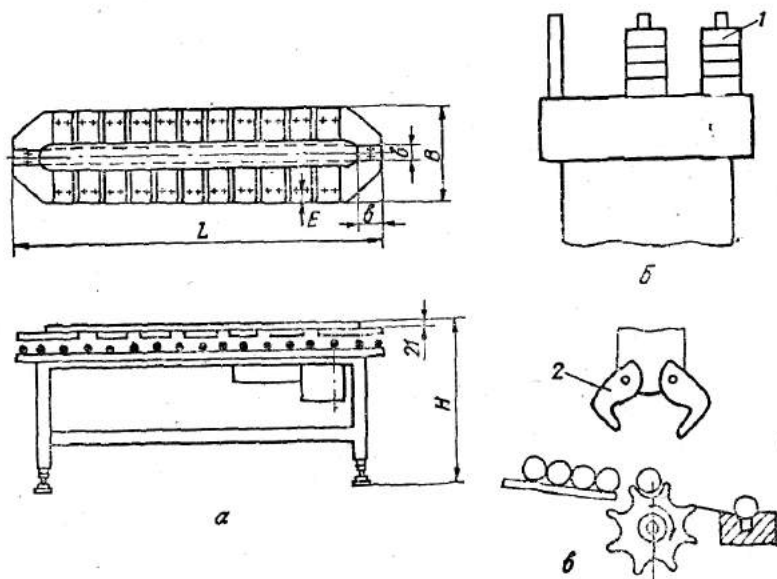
Магазины, які забезпечують подавання заготовки 1 в точку захоплення 2 промисловим роботом: а — тактовий стіл; б — поворотний стіл; в — лотік.
